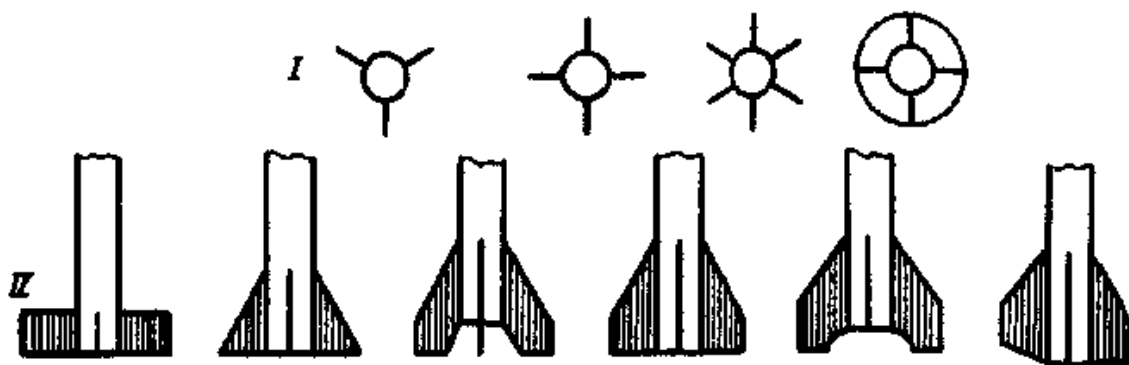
Виды хвостового оперения: I – вид сверху, II – вид сбоку.
